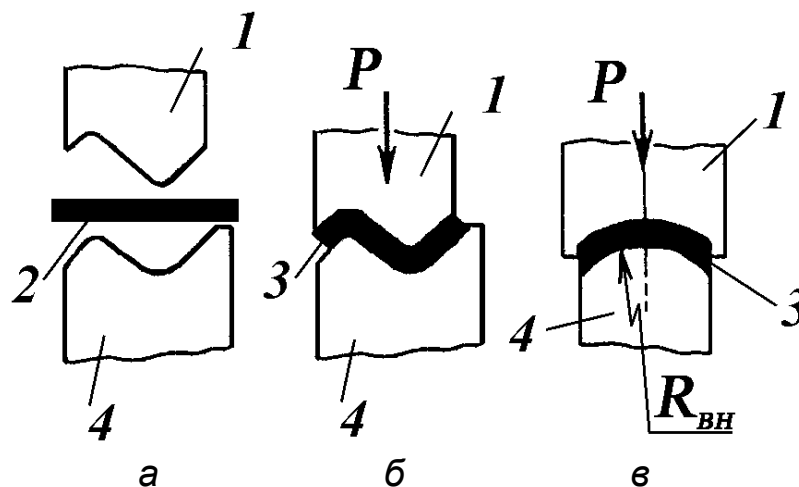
Схеми згинання: а – початкове положення; б – згинання зі зміною кутів між частинами заготовки; в – згинання з наданням криволінійної форми (1 – згинальний пуансон; 2 – заготовка; 3 – готова деталь; 4 – матриця)
